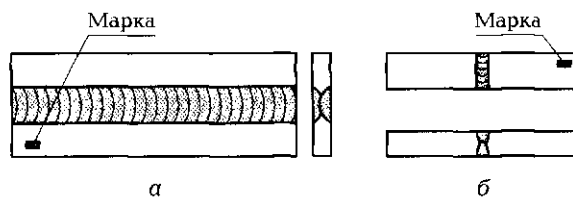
Образцы для испытаний на изгиб с продольным (а) и поперечным (б) швами
